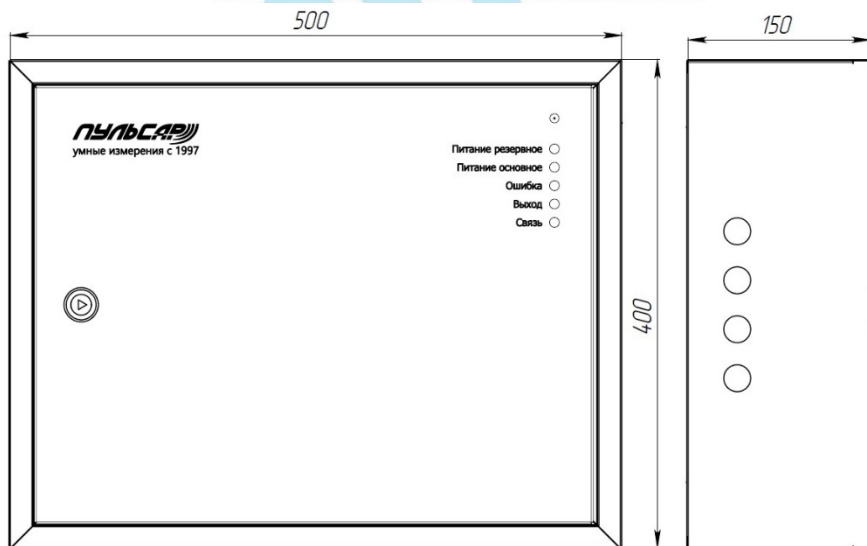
Габаритные размеры и маркировка ИБЭ
